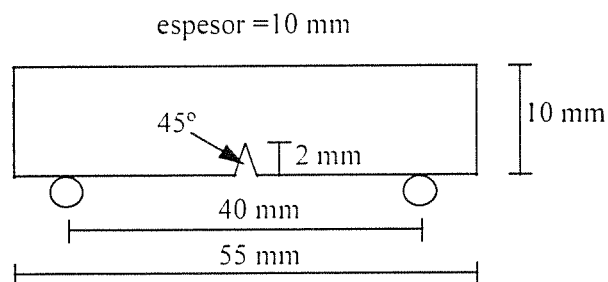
Geometría y dimensiones de las probetas ensayadas.
